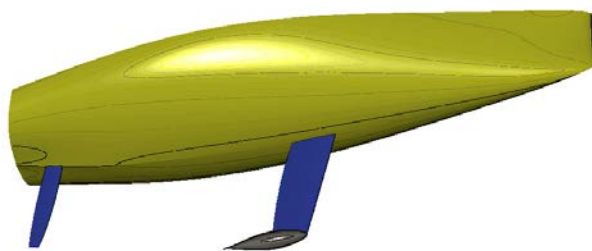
3D-модель поверхні корпусу яхти з радіальними обводами
